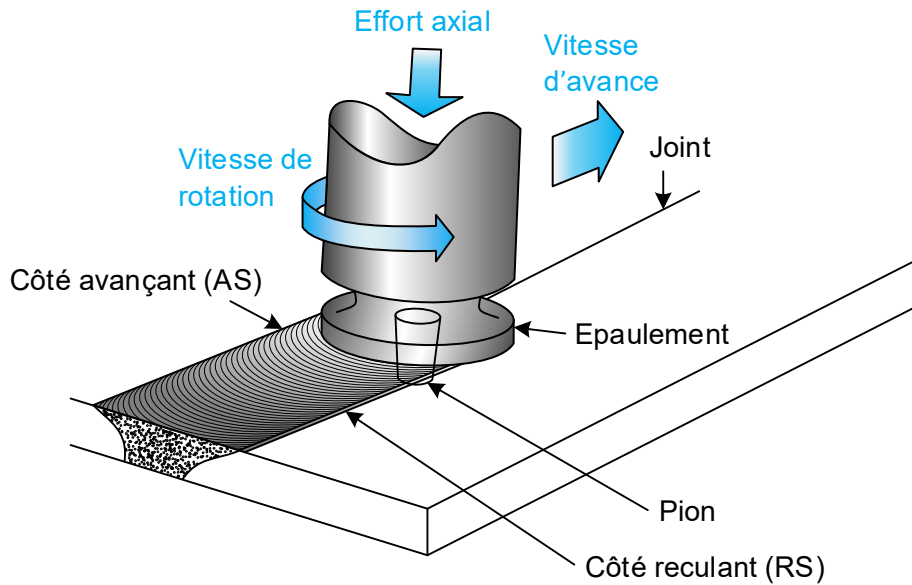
Schéma de principe du procédé de soudage par friction malaxage [51].
